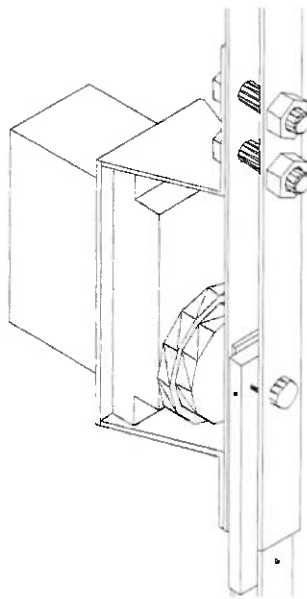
Desenho de conjunto do tornozelo – vista frontal
